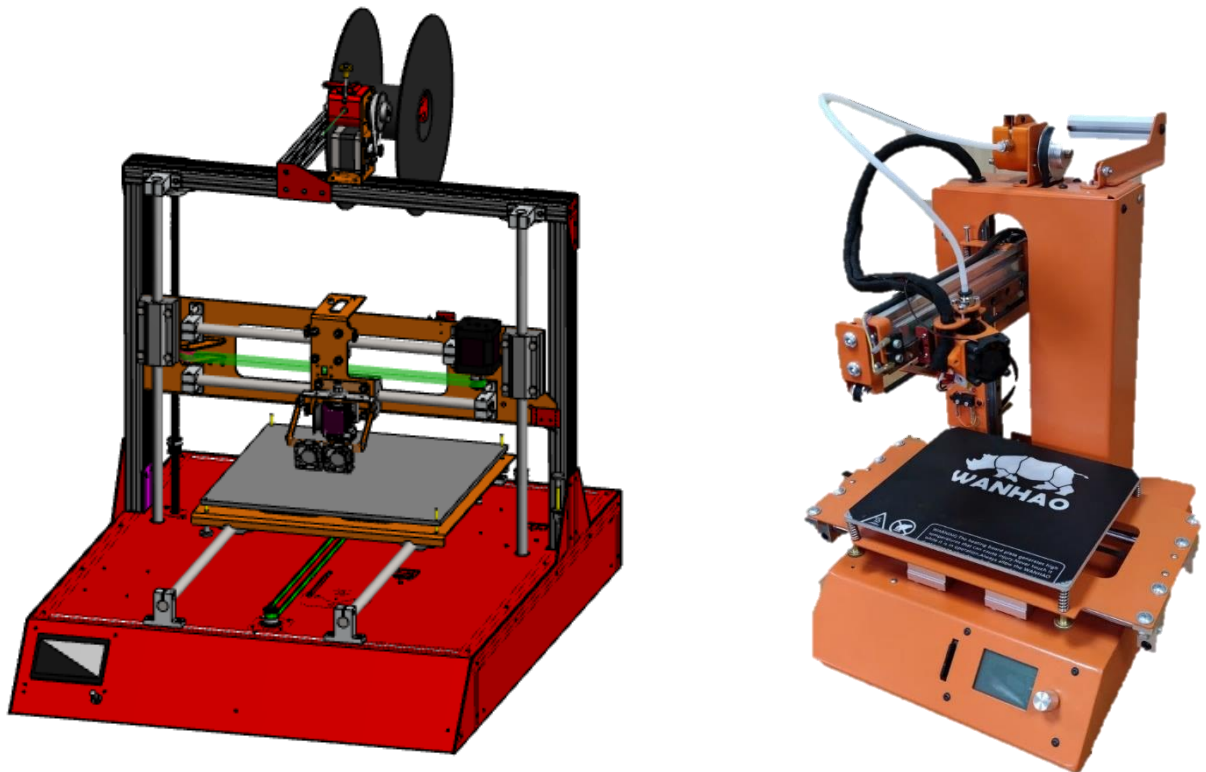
Конструкція 3D-принтера друкуюча за методом пошарового наплавлення (FDM).
